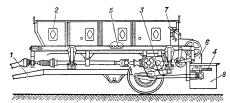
Разбрасыватель минеральных удобрений: 1 — шасси; 2 — кузов; 3 — главный редуктор; 4 — разбрасывающее устройство; 5 — цепочно-планчатый транспортёр; 6 — тукоотделитель; 7 — дозирующее устройство; 8 — ветрозащитное устройство.
